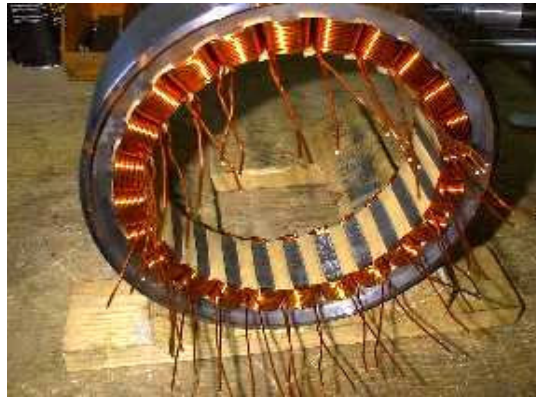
Bobinage concentré pour une machine à flux radial [23].
